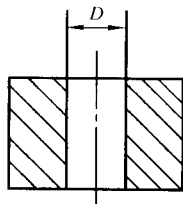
工件预加工尺寸和螺纹尺寸关系
